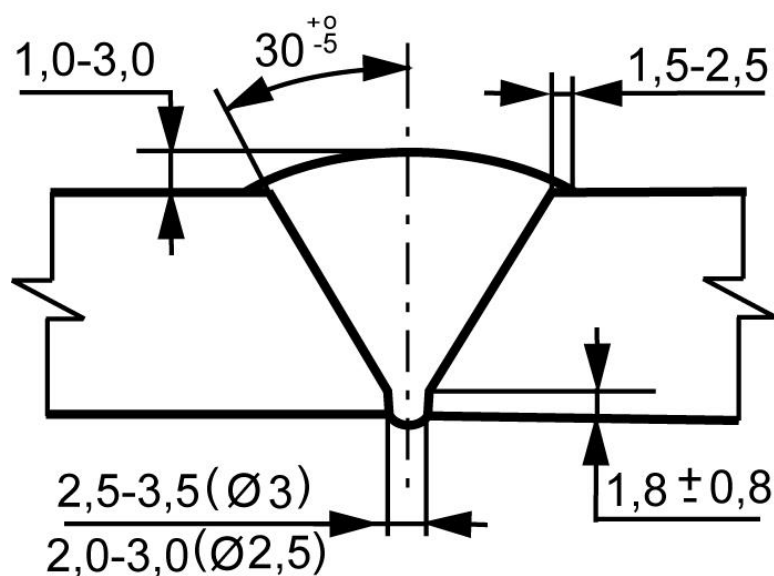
Форма разделки кромок и сварного шва.
